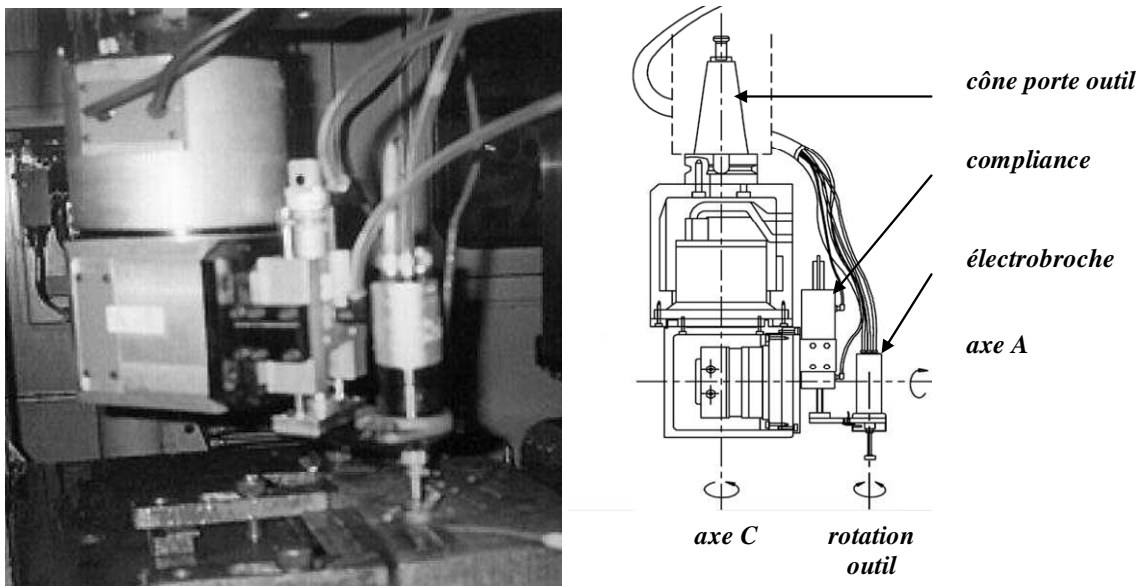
Tête de ponçage 2 axes montée sur une machine CN [LGCL_02]
